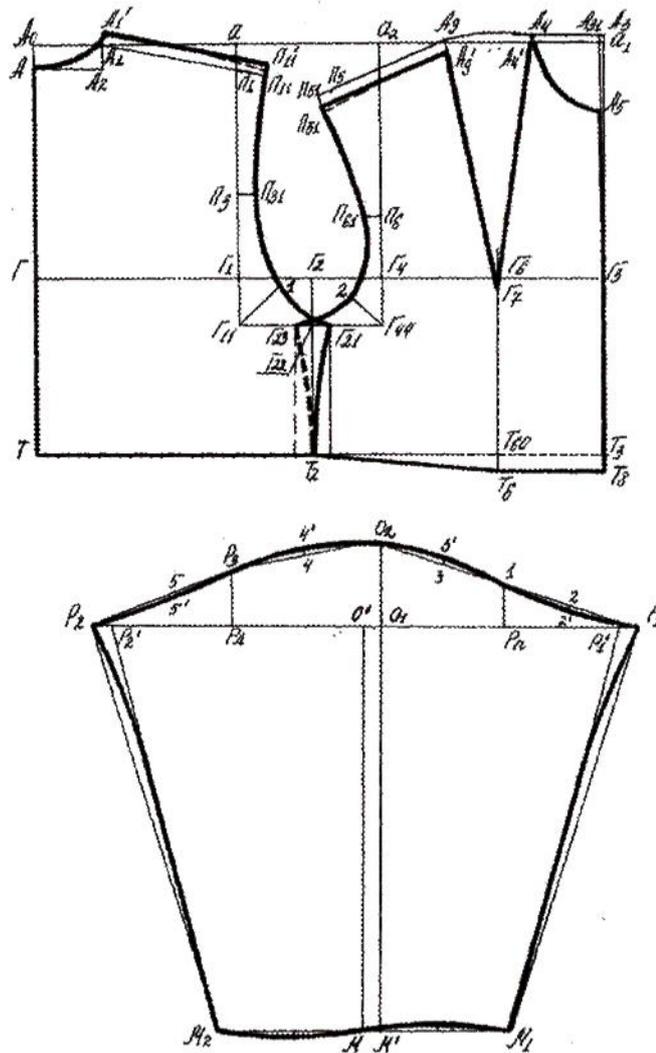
Чертеж конструкции изделия и рукава рубашечного покроя с овальной проймой.
